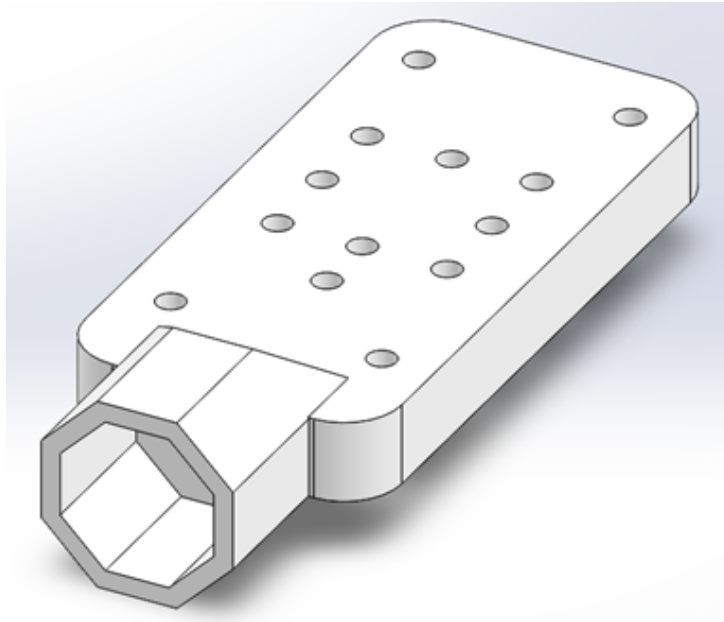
Sujetador de motor en vista isométrica. Fuente: Propia.
